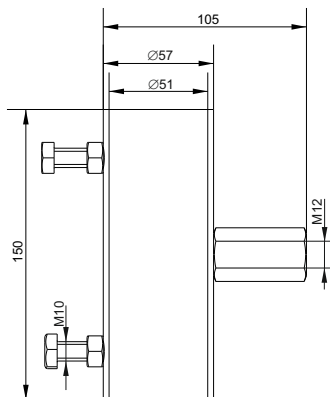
Габаритные размеры держателя / Figure 1 – Overall dimensions of the holder /
